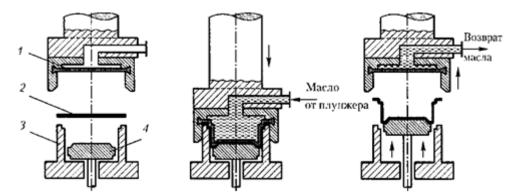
Схема гидроформования с эластичной мембраной: 1 – мембрана; 2 – заготовка; 3 – матрица; 4 – оформляющий выталкиватель
